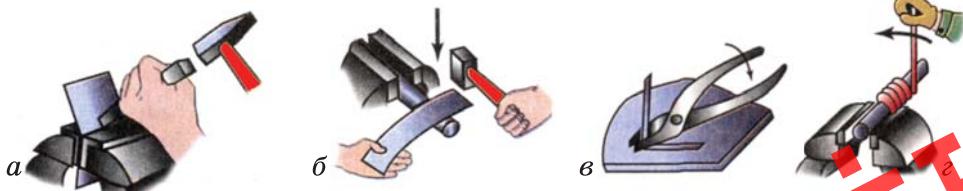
Сгибание заготовки: а – в тисках; б – на оправке; в – круглогубцами; г – в гибочном приспособлении
